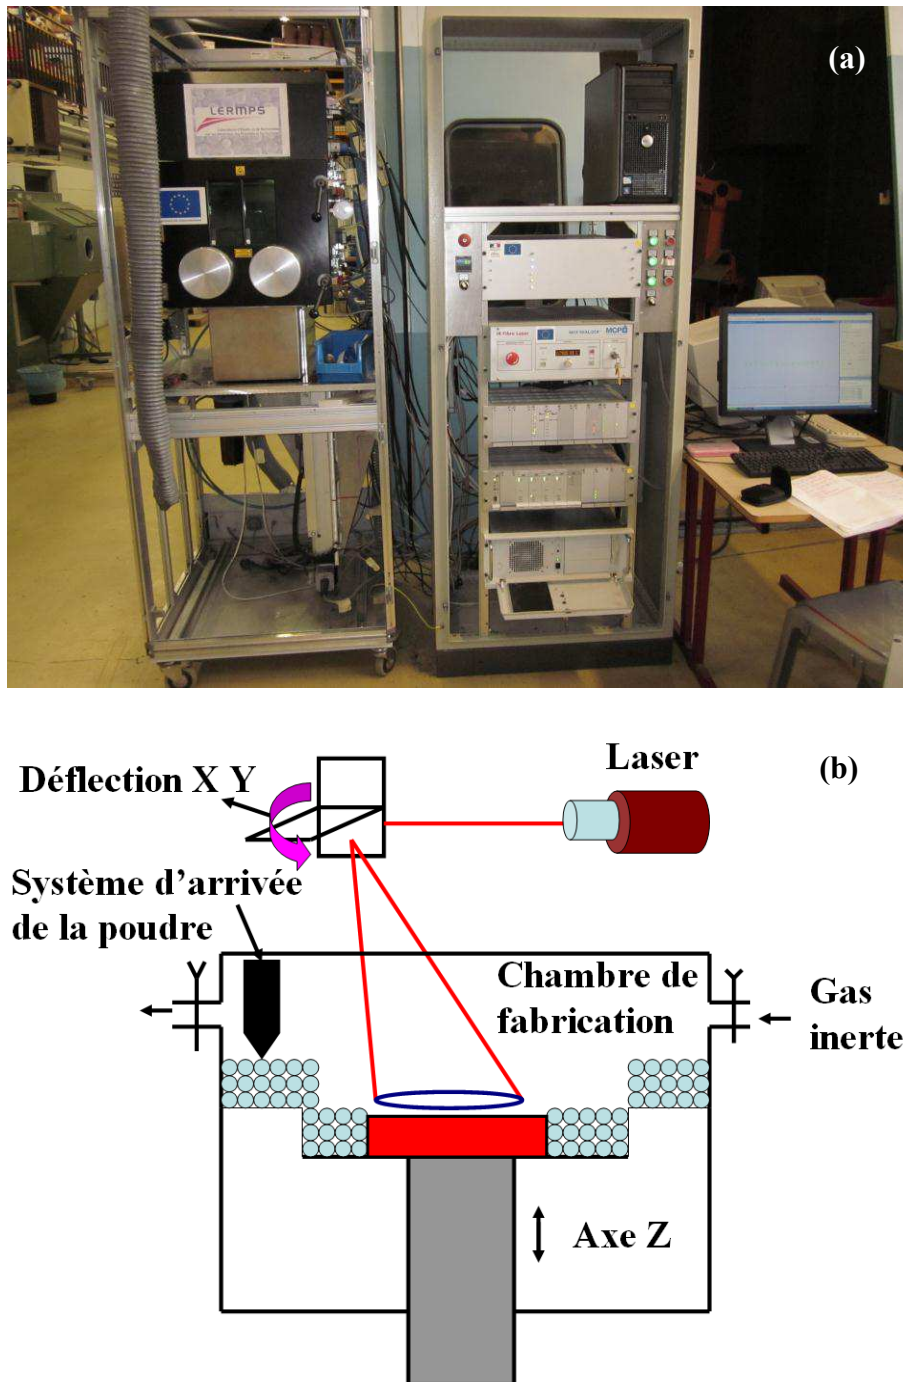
(a) Photographie de l'équipement SLM, (b) schéma de principe de la machine.
